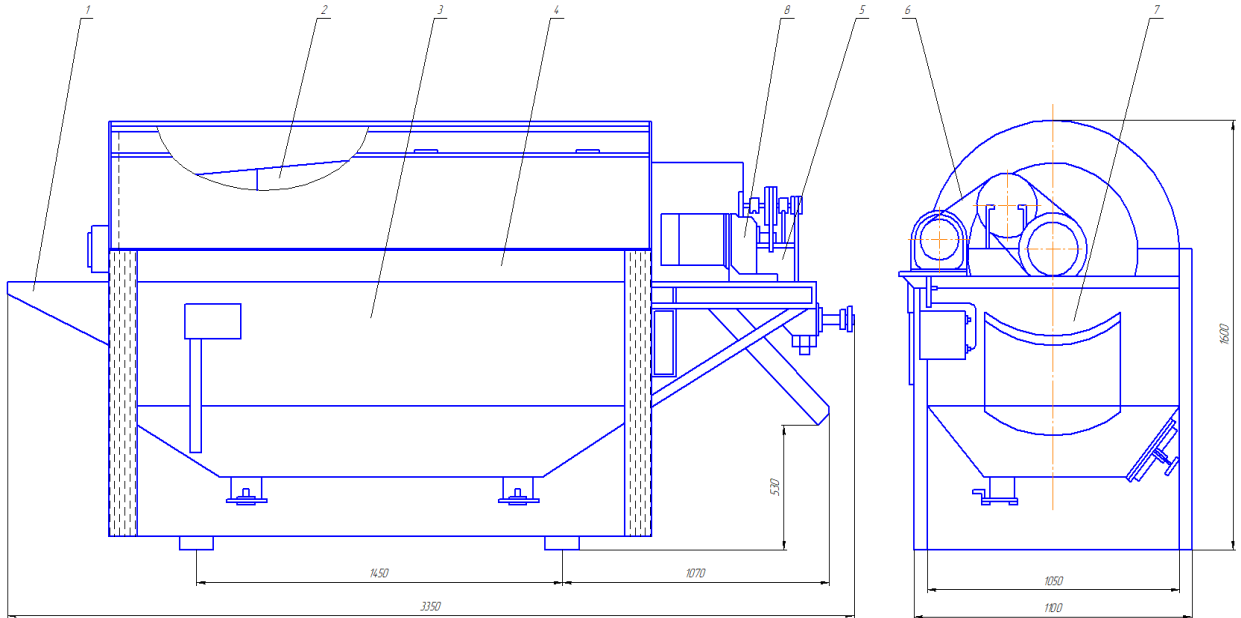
Вдосконалена мийна машина А9-КМ-2: 1 - завантажувальний лоток; 2 - мийний барабан; 3 – кожух; 4 – каркас; 5 – редуктор; 6 - ланцюгова передача; 7 - вивантажувальний лоток; 8 - привід.
